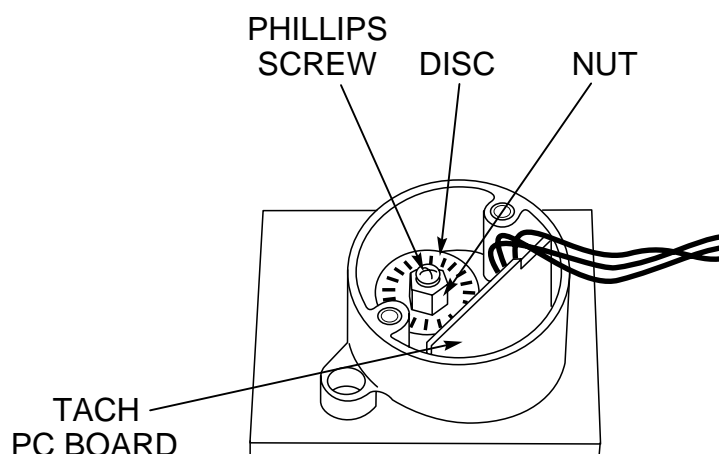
DISCO GIRATORIO, TUERCA Y TARJETA DEL TACÓMETRO
